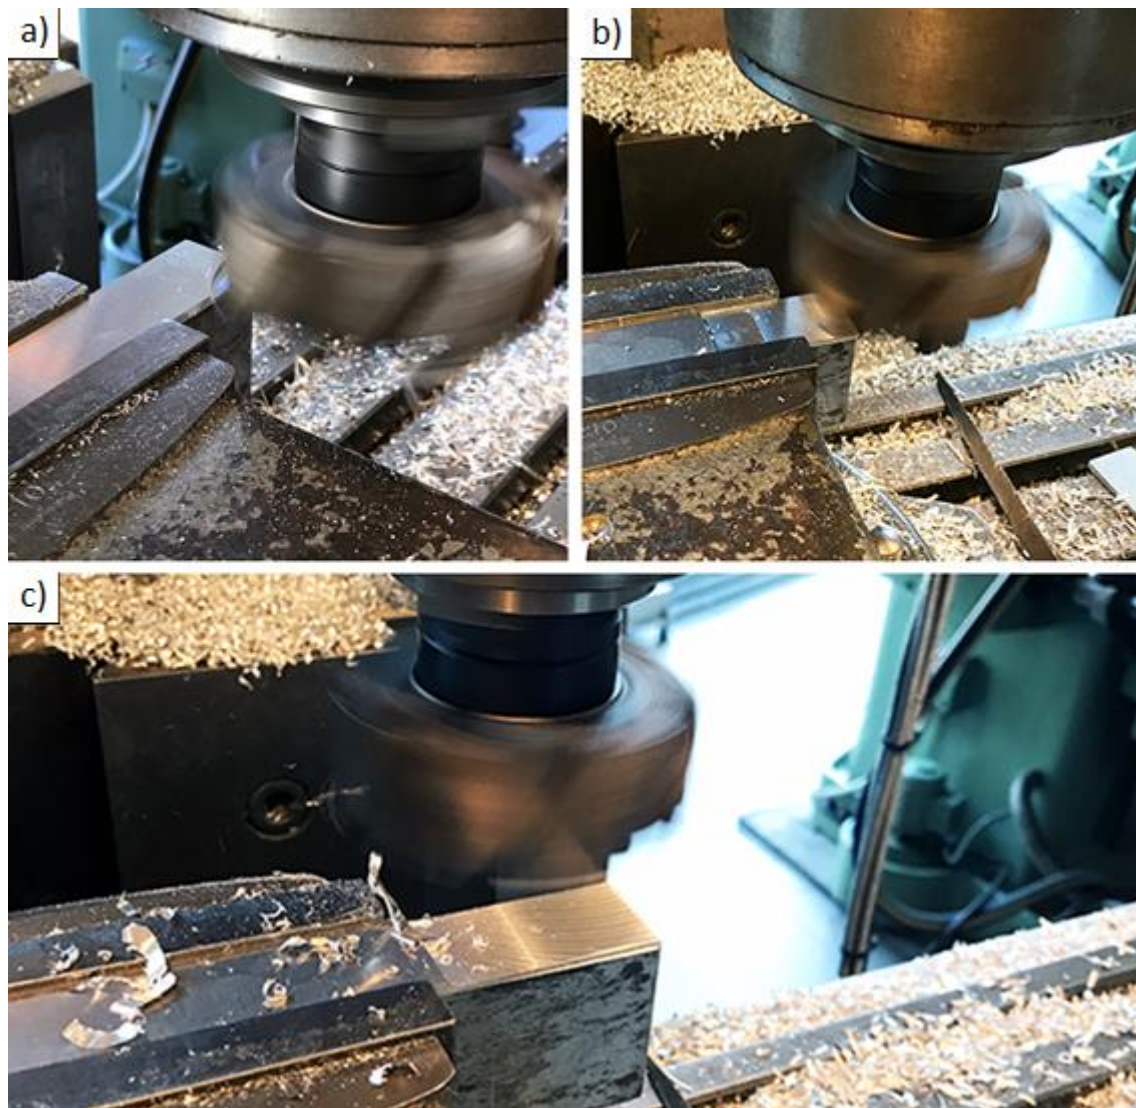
Diferentes etapas do processo de maquinagem: a) início do ataque da fresa; b) primeira passagem da fresa e c) segunda passagem da fresa.
